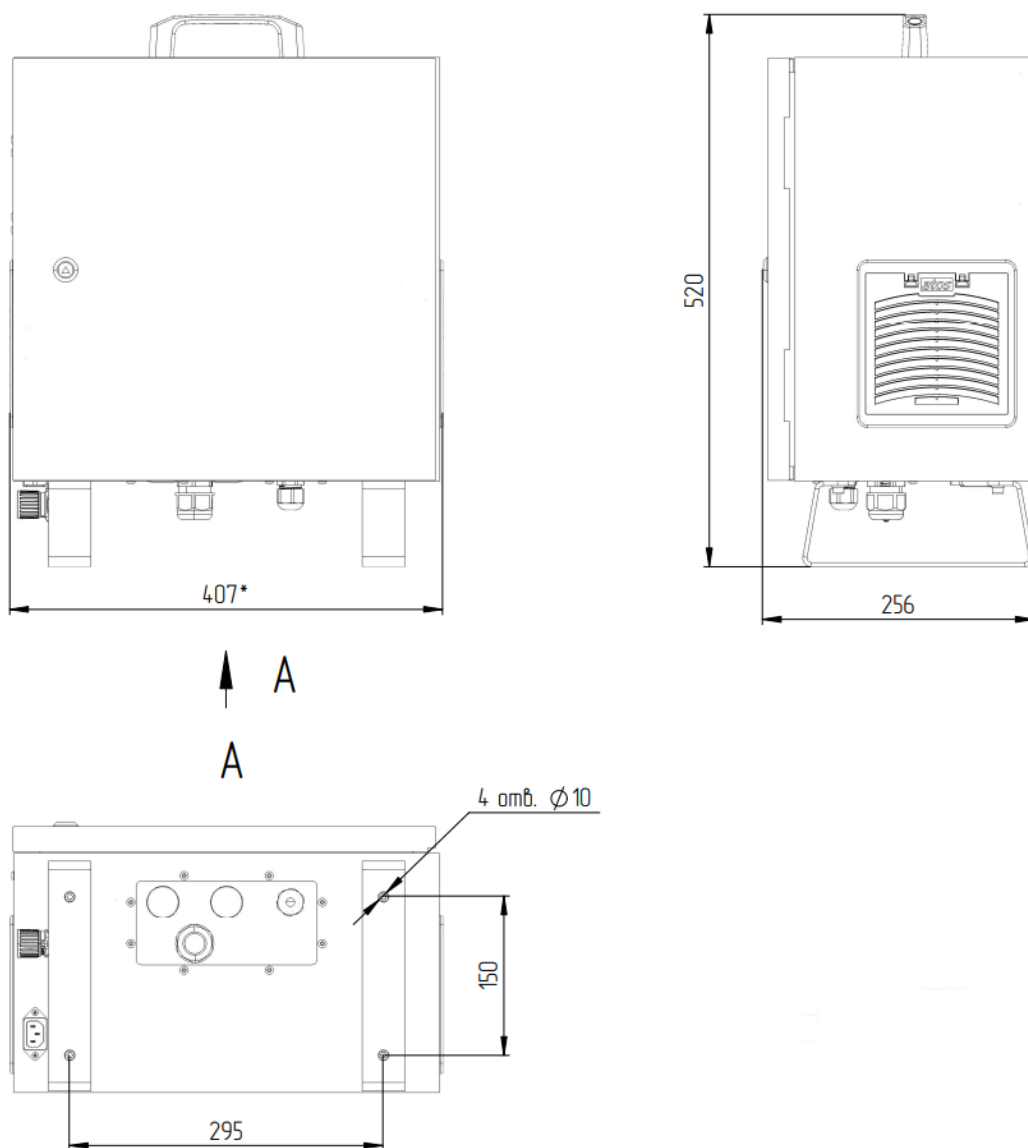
Габаритные размеры контроллера робота 3.6
